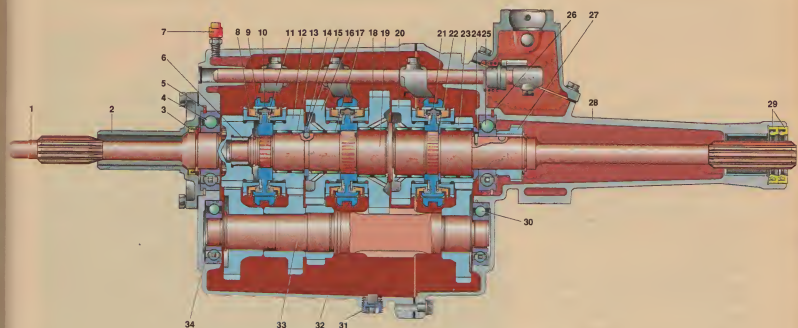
Пятиступенчатая коробка передач: 1 – первичный вал; 2 – крышка подшипника первичного вала; 3 и 29 – сальники; 4 – шариковый подшипник первичного вала; 5 – стопорное кольцо; 6 – роликовый подшипник вторичного вала; 7 – сапун; 8 – блокирующее кольцо; 9 – муфта включения; 10 – сухарь синхронизатора; 11 – ступица муфты включения III и IV передач; 12 – шестерня III передачи; 13 – игольчатый подшипник шестерни; 14 – стопорное кольцо полуколец; 15 – полукольцо; 16 – шестерня II передачи; 17 – стопорное кольцо; 18 – шестерня I передачи; 19 – вторичный вал; 20 – шестерня заднего хода; 21 – ступица муфты включения V передачи и заднего хода; 22 – стопорное кольцо; 23 – шестерня V передачи; 24 – упорная шайба; 25 – шариковый подшипник вторичного вала; 26 – стопорное кольцо; 27 – ведущая шестерня привода спидометра; 28 – задний картер; 30 – шариковый подшипник блока шестерен; 31 – сливная пробка; 32 – передний картер; 33 – блок шестерен; 34 – регулировочная прокладка.
